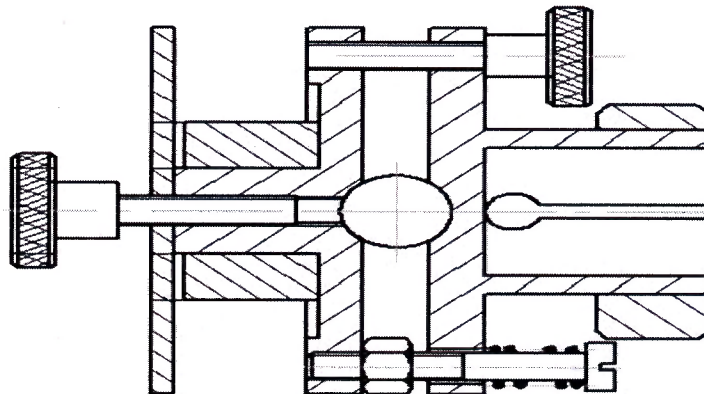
приспособление для установки многогранной призмы с присоединительным диаметром 12 или 20 мм.
